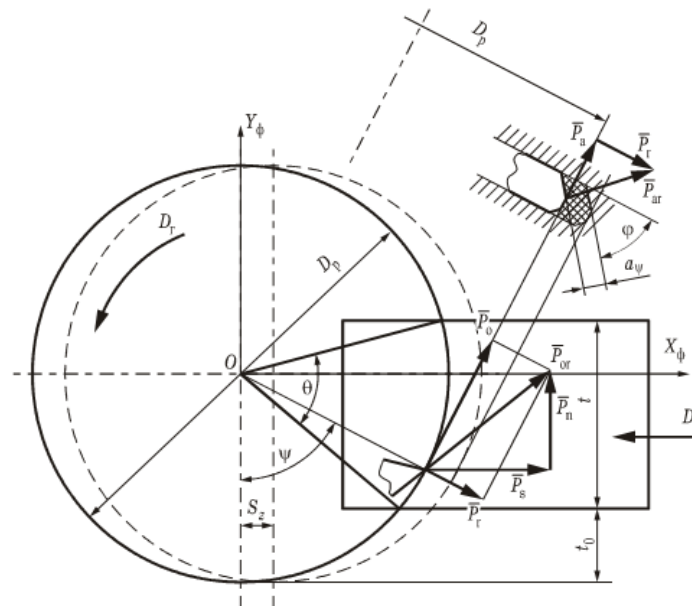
Схема дії сил на зубці при фрезеруванні дисковою фрезою
